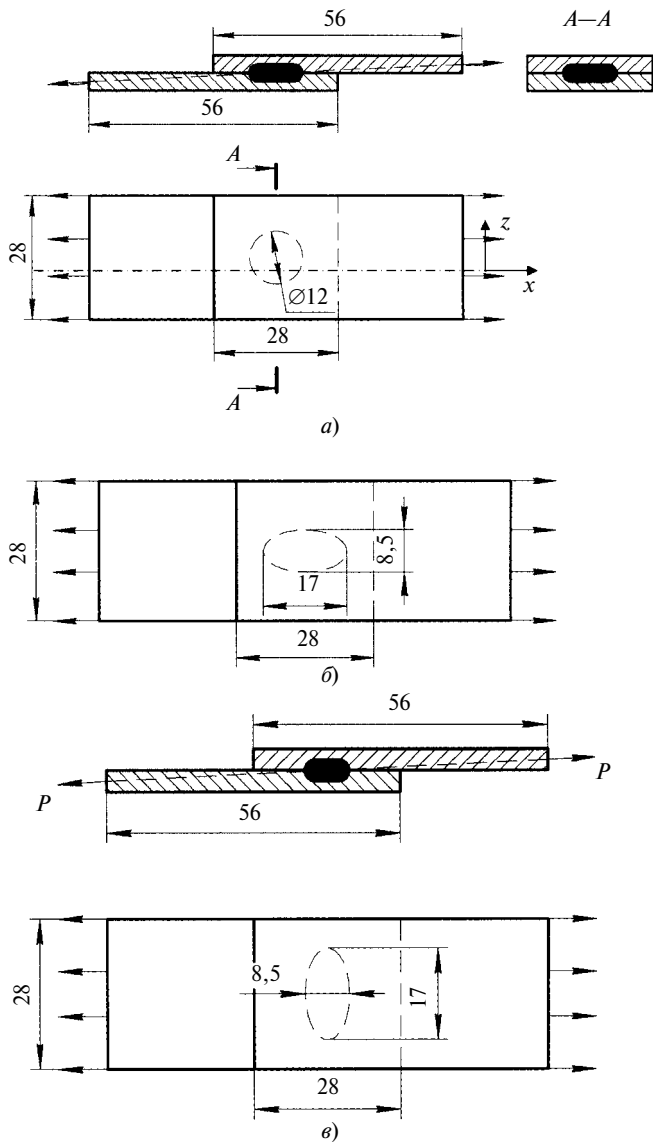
Схемы точечных сварных соединений с круглой (а), овальной продольной (б) и овальной поперечной (в) точками
